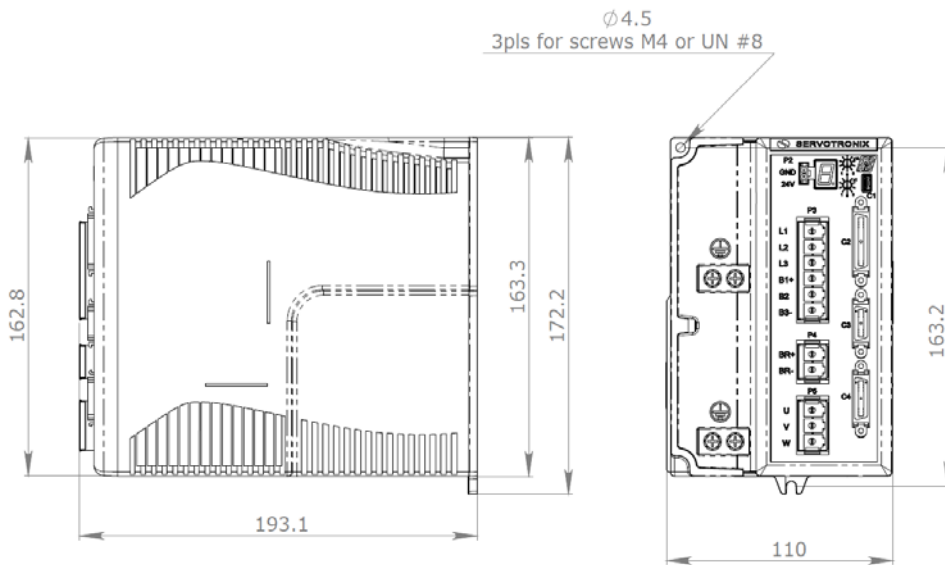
CDHD-003/CDHD-006 - 400/480 VAC - 外形尺寸 (mm)
